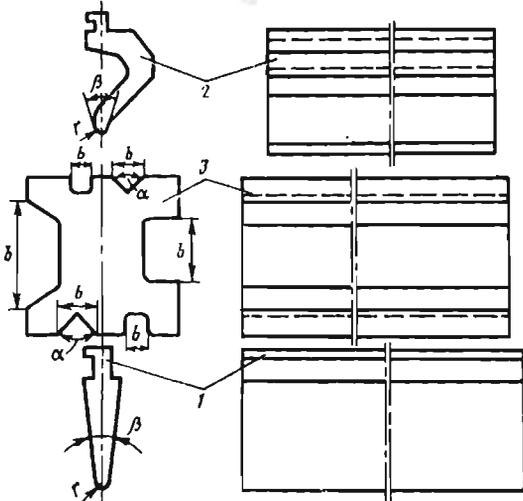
Детали универсального гибочного штампа для гибки профилей из полос: 1 — прямой пуансон; 2 — изогнутый пуансон; 3 — матрица
